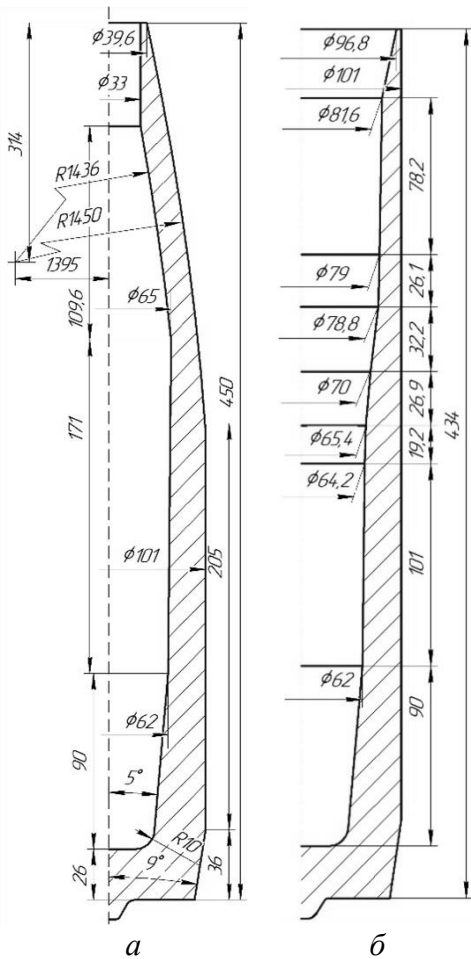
Ескізи половин виробу (а) і заготовки (б)
